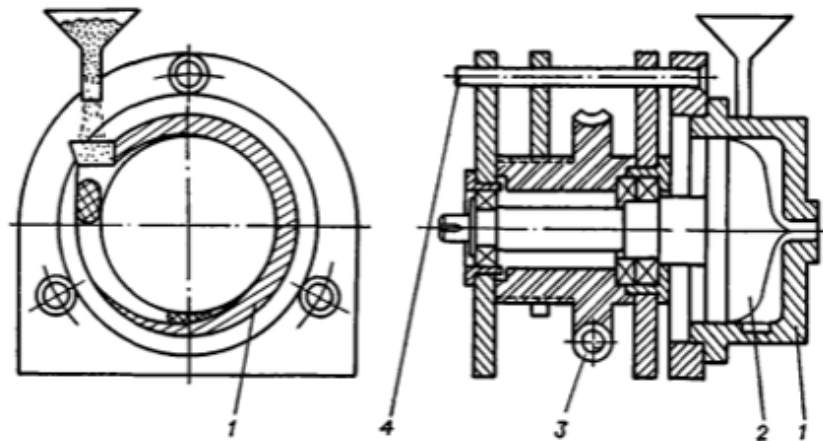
Схема дискового екструдера: 1 - корпус; 2 - диск; 3 - черв'ячна передача; 4 – напрямні
